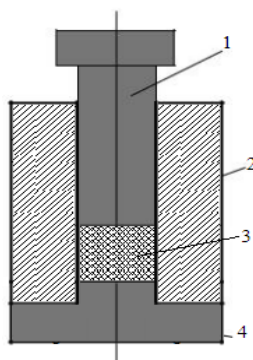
Схема пресс-формы для одностороннего холодного прессования порошков: 1 – пуансон верхний; 2 – матрица; 3 – порошок; 4 – пуансон нижний (неподвижный)
